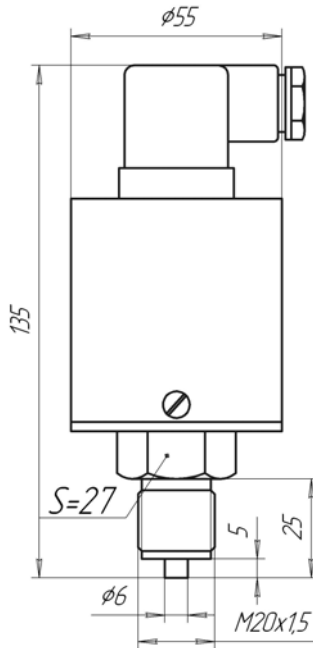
Модель 1025. Алюминиевый корпус, герморазъем.
